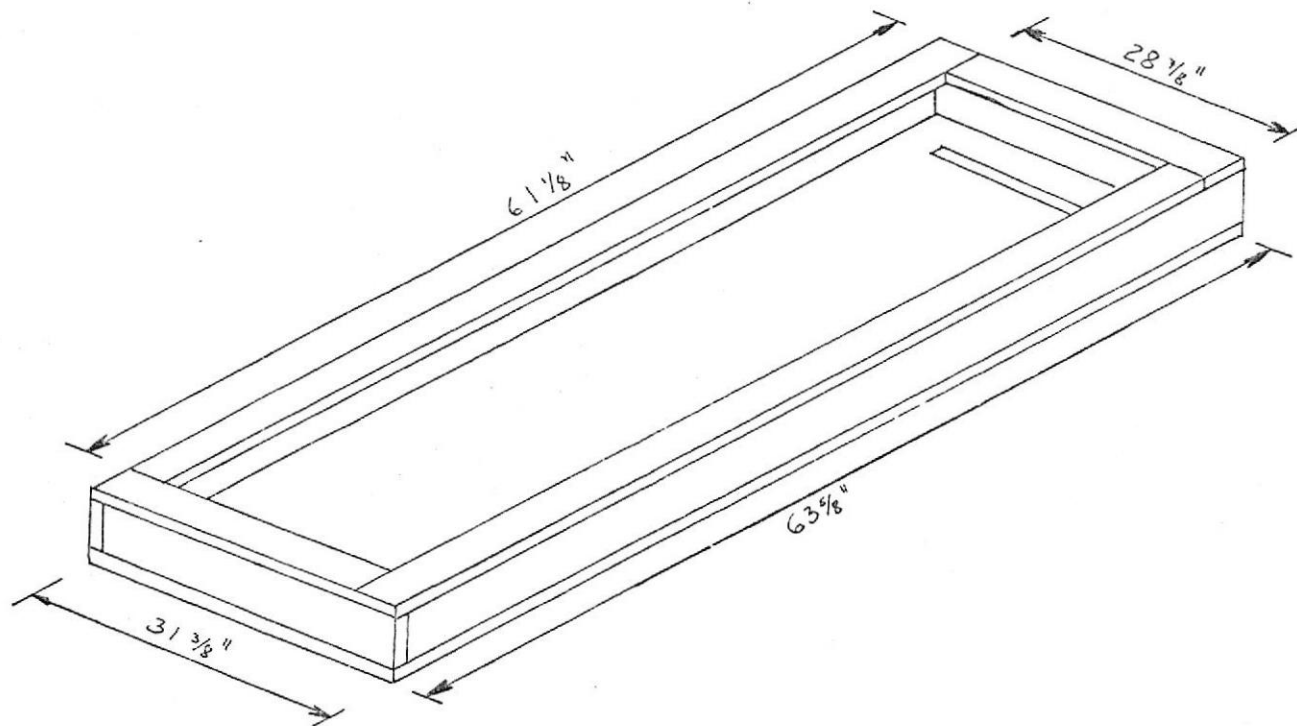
DIMENSIONES DE LA CAJA DE MADERA
